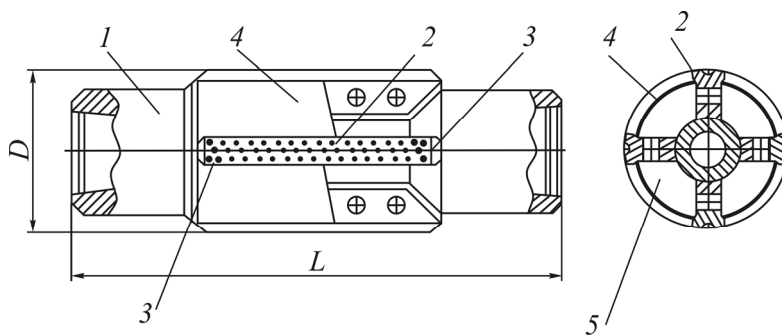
Конструктивная схема металлоуловителя-калибратора ИСКМ – МУК-212,7
